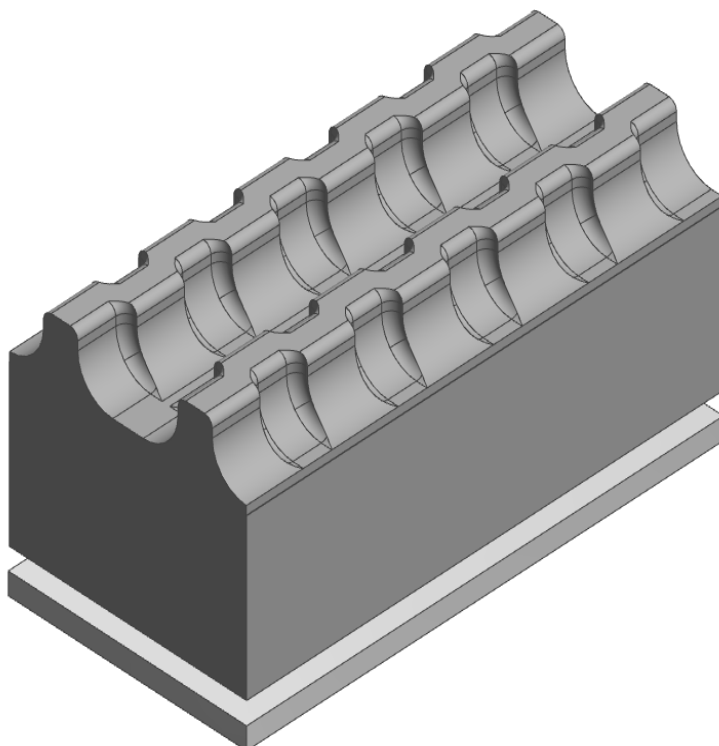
Model testovacího obrobku č.4. „symetrické schody“.
